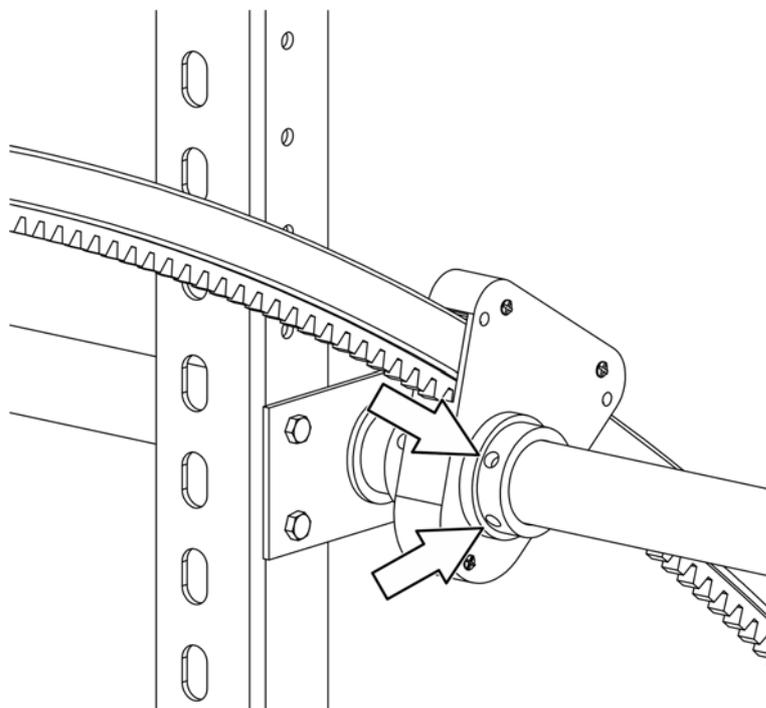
Löcher zum Eindrehen der Madenschrauben
